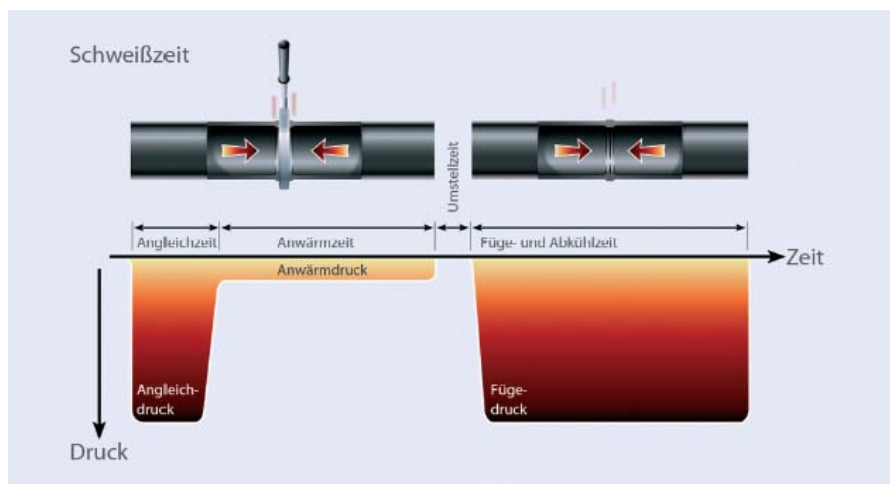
Zeitlicher Ablauf des Heizelementstumpfschweißens gemäß DVS 2207-1
